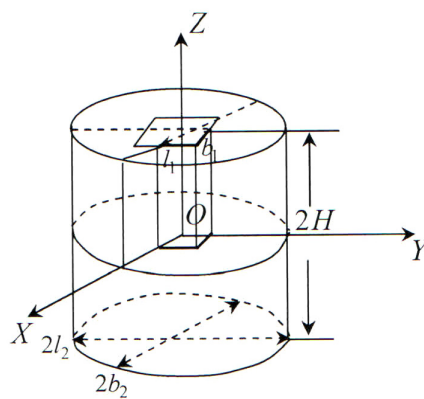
Деталь с эллиптической поверхностью и прямоугольным отверстием
